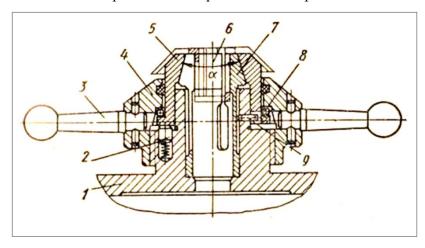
Приспособление с цанговым центрирующим устройством
